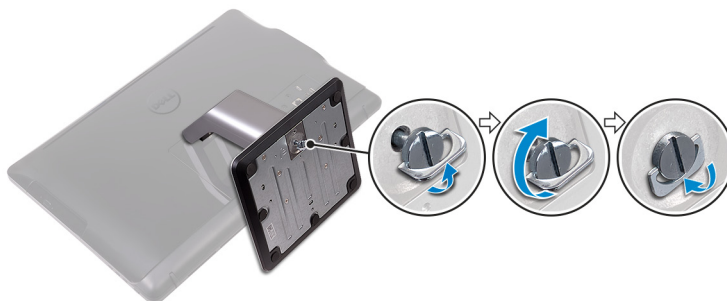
Serrer la vis imperdable pour fixer la base au socle
